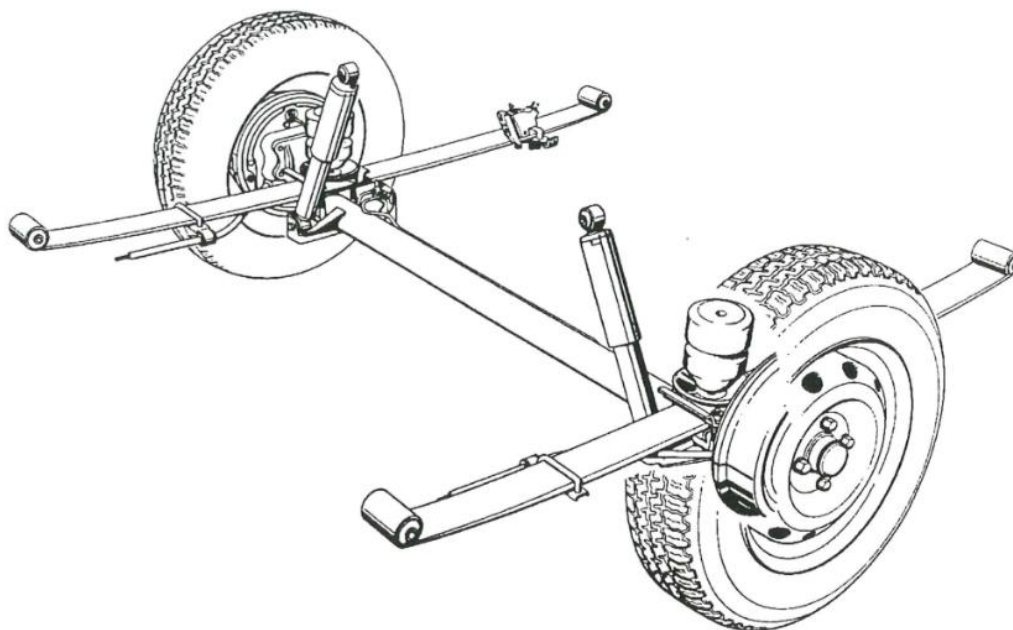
Hnací a hnaná náprava [upraveno dle 24]
